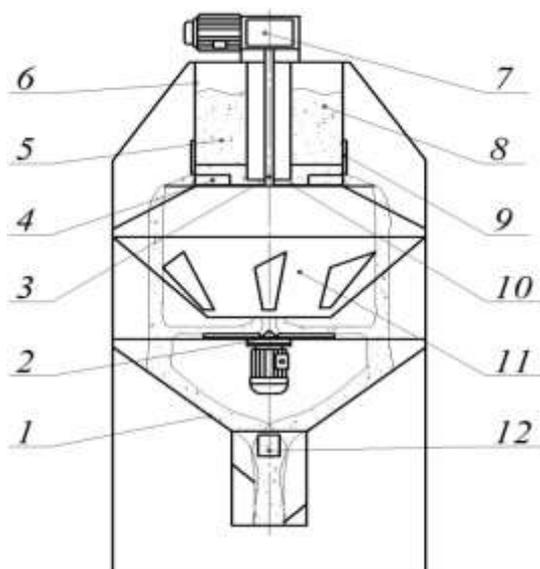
Схема дозатора-смесителя сыпучих кормов:
